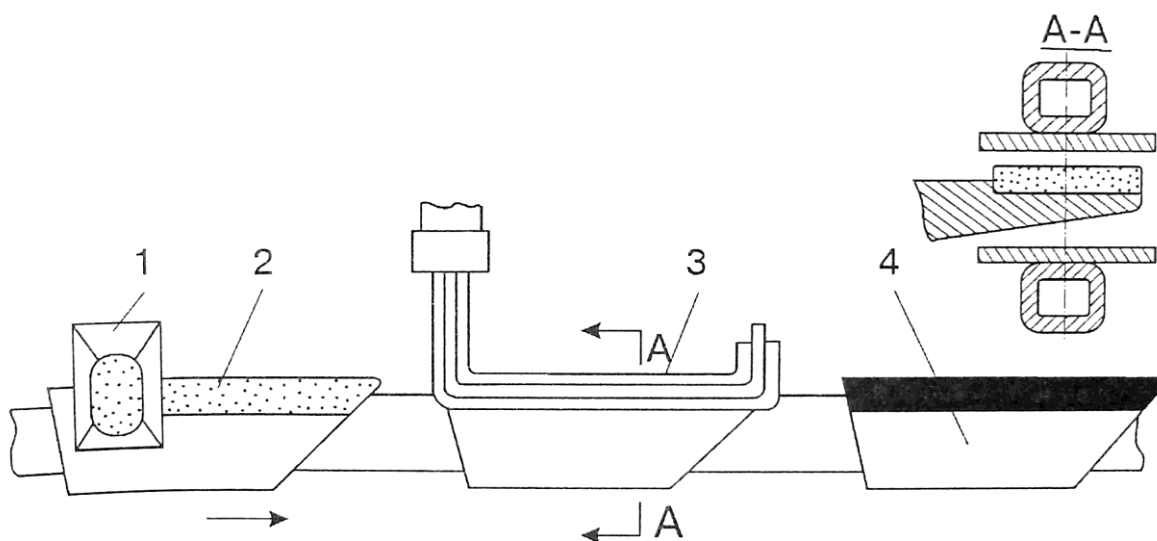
Схема индукционной наплавки лемеха с использованием порошковой шихты:
